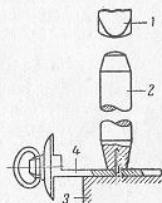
Осадка металла вокруг отверстия для соска боевой пружины:
